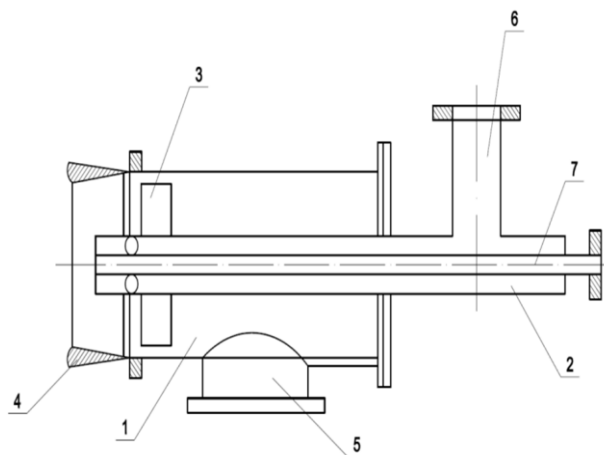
Конструкция газовых горелок: 1 – воздушная камера; 2 – газовая камера; 3 – завихритель; 4 – насадок горелки; 5 – воздушный патрубок; 6 – газовый патрубок; 7 – смотровая труба
